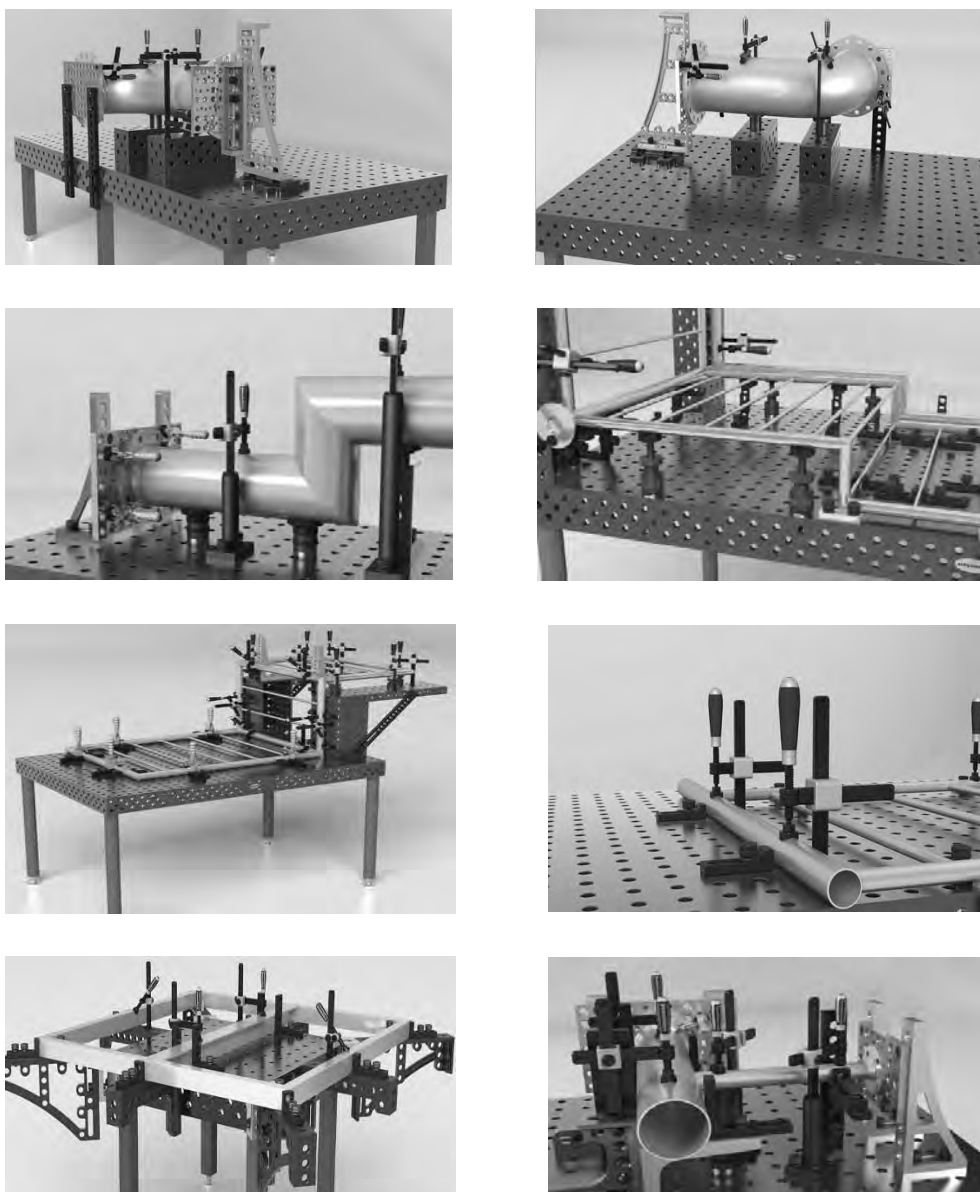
Сборка узлов на сварочных столах Siegmund (Германия)
